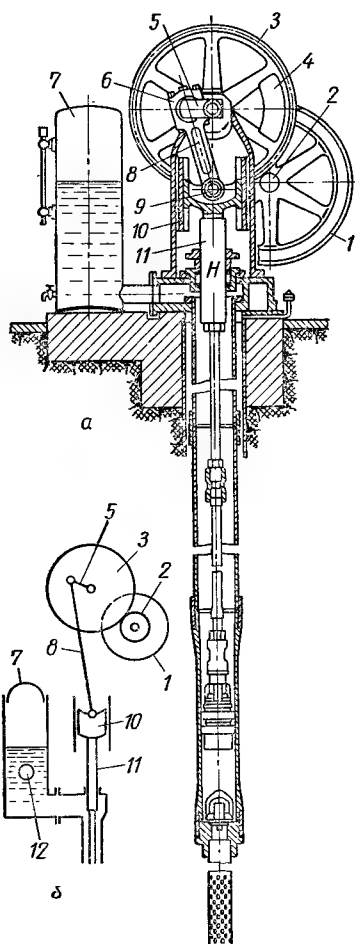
Лебедка без рычажного балансирующего устройства (а) и схема привода поршневого насоса (б):
